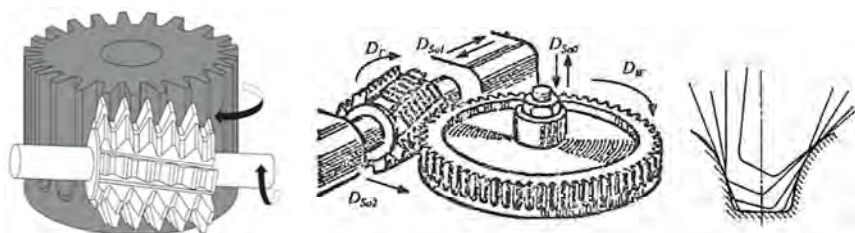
Схема работы червячной зуборезной фрезы и образования профиля зубьев
